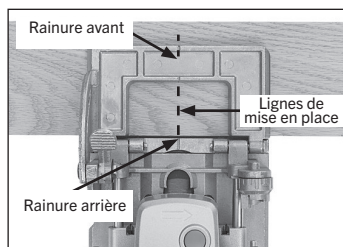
Machine à jointer alignée avec la pièce à usiner.
